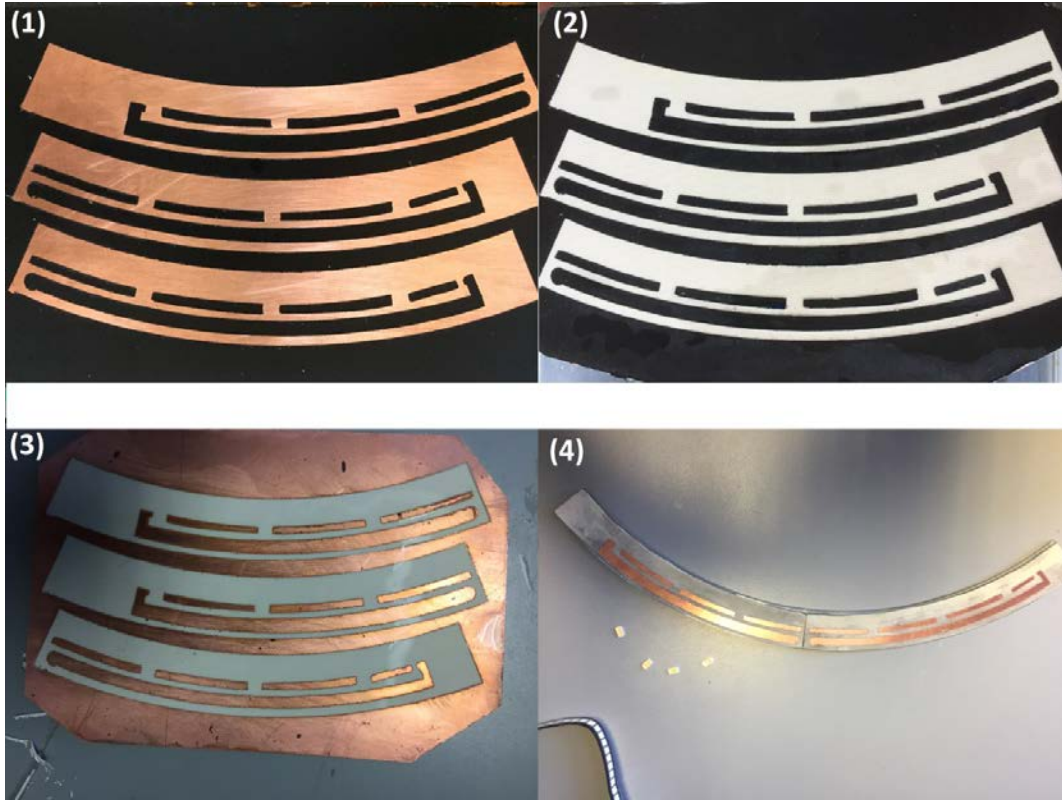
Método de trazado de pistas en PCB para obtener la geometría deseada.
